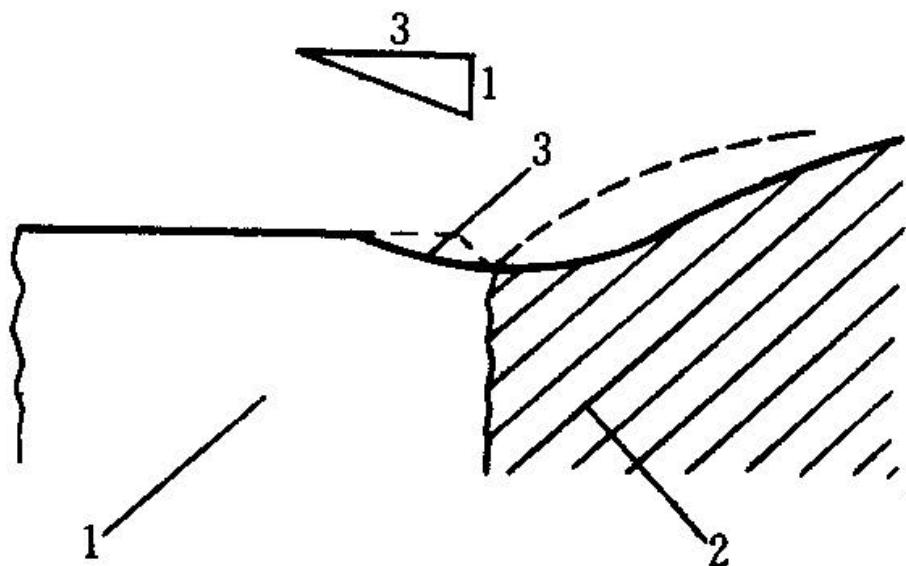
1 焊缝两侧的焊接缺陷用砂轮修磨
